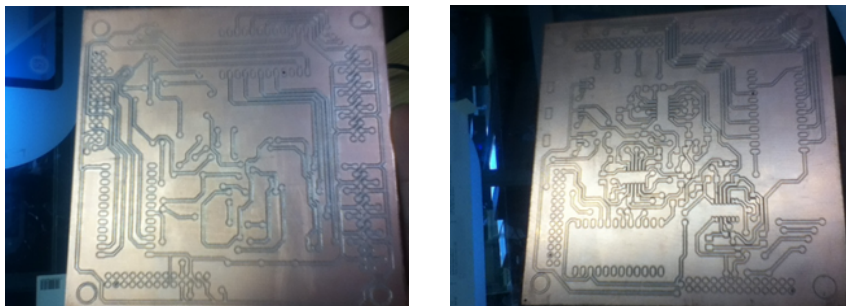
PCBs fabricadas con CNC en Juriquilla
